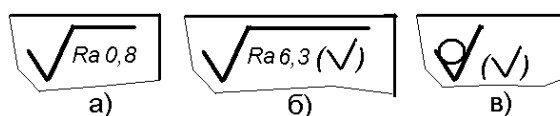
Примеры обозначения шероховатости поверхностей в правом верхнем углу чертежа
